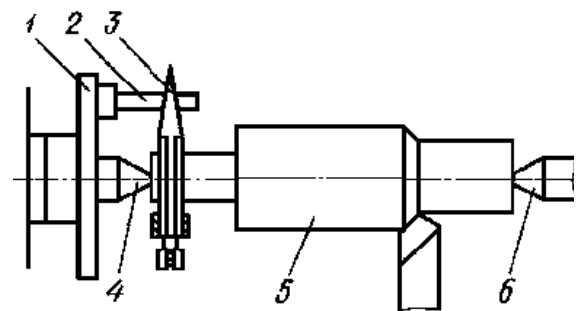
Повідковий патрон (1 – планшайба, 2 – водило, 3 – поводок, 4 – глухий центр шпинделя, 5 – заготовка, 6 – центр задньої бабки)
